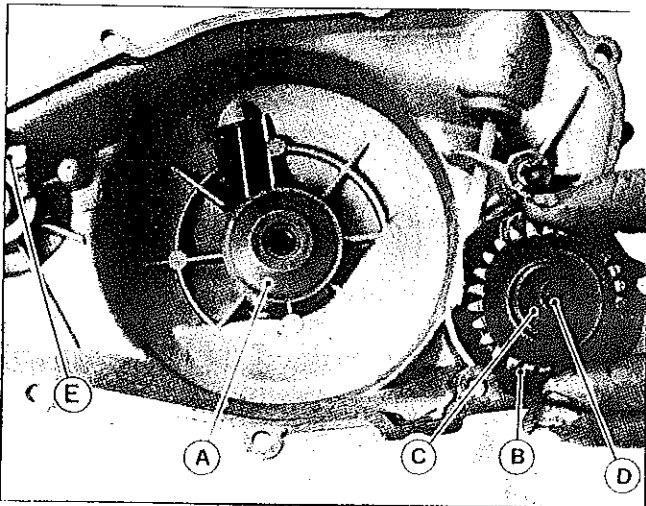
A. CONJUNTO ACIONADOR DA MOLLA
